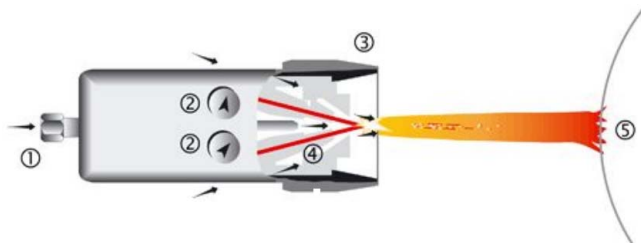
Схема дугового напыления: 1 — распыляющий газ; 2 — подача проволоки регулируемая; 3 — сопло; 4 — электропроводящая проволока; 5 — деталь
